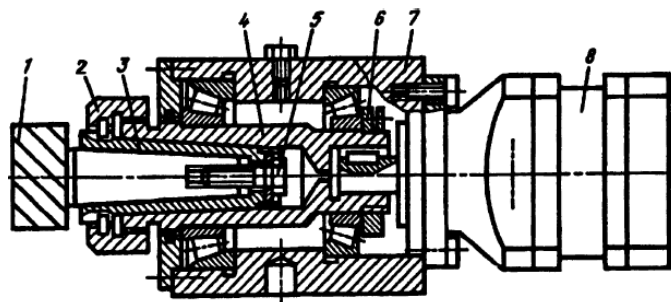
Фрезерна головка: 1 – фреза; 2 – гайка; 3 – втулка; 4 – шпиндель; 5 – болт; 6 – кільце; 7-корпус; 8 – вал.
